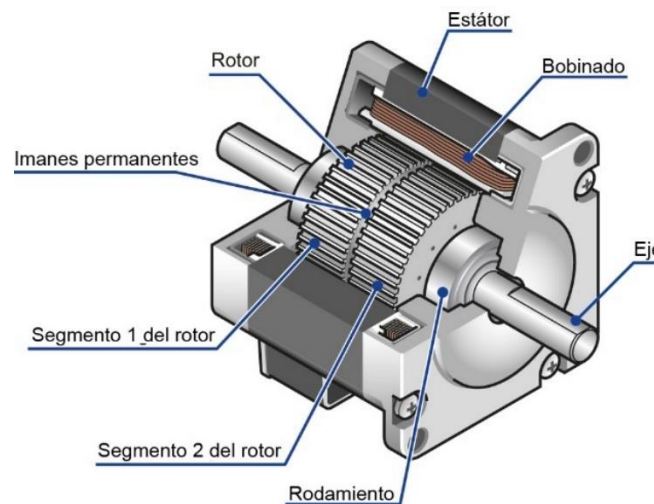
Estátor, rotor, imanes permanentes y bobinados son los principales componentes de un motor paso a paso.
